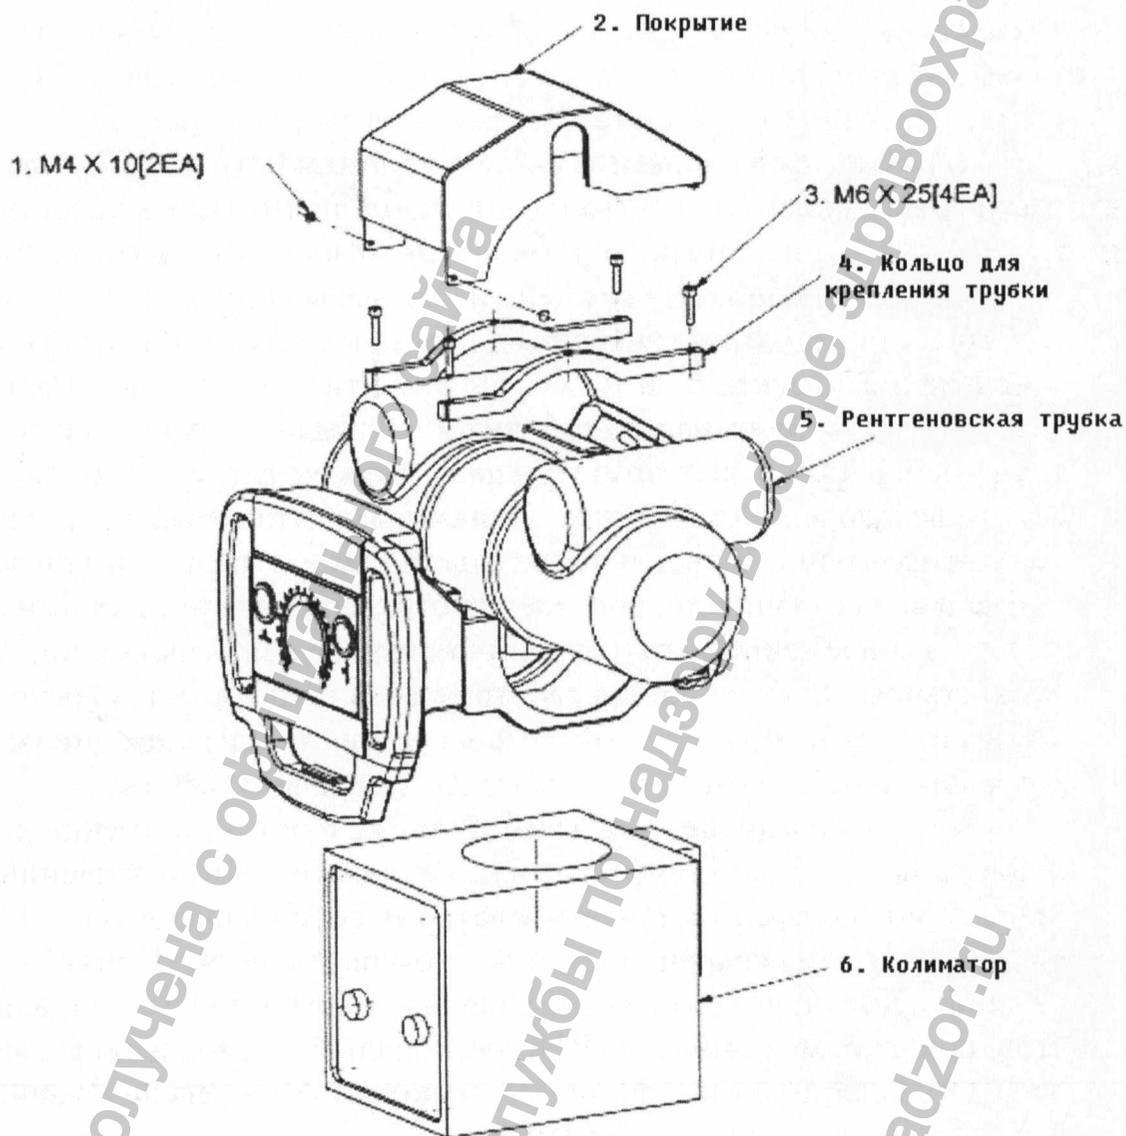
Установка рентгеновской трубки и коллиматора
